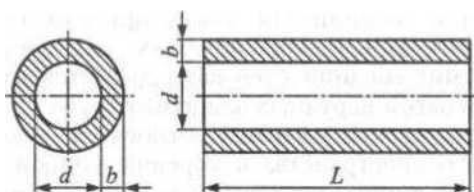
Общий вид термоусаживаемой трубки: L - длина; d - внутренний диаметр; b - толщина стенки
